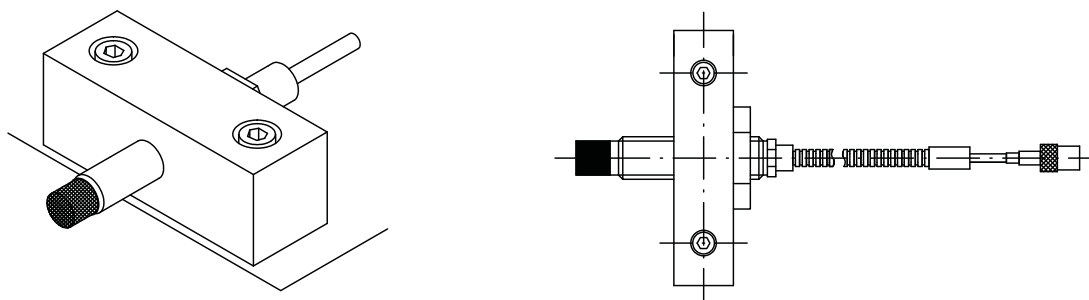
Монтажная подложка (с просверленным резьбовым отверстием) для стандартного преобразователя перемещений
